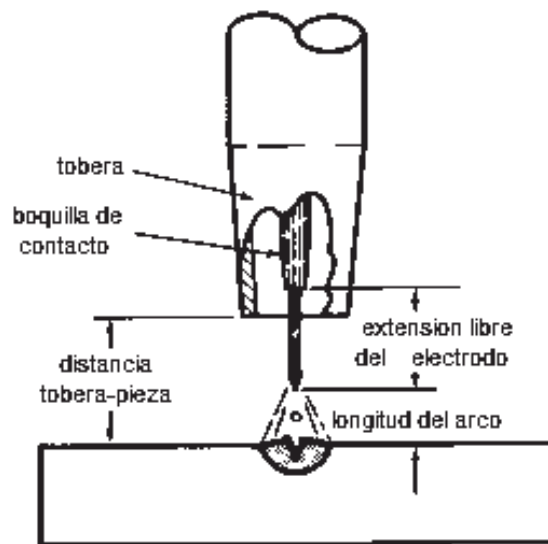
Terminología del proceso de soldadura GMAW
